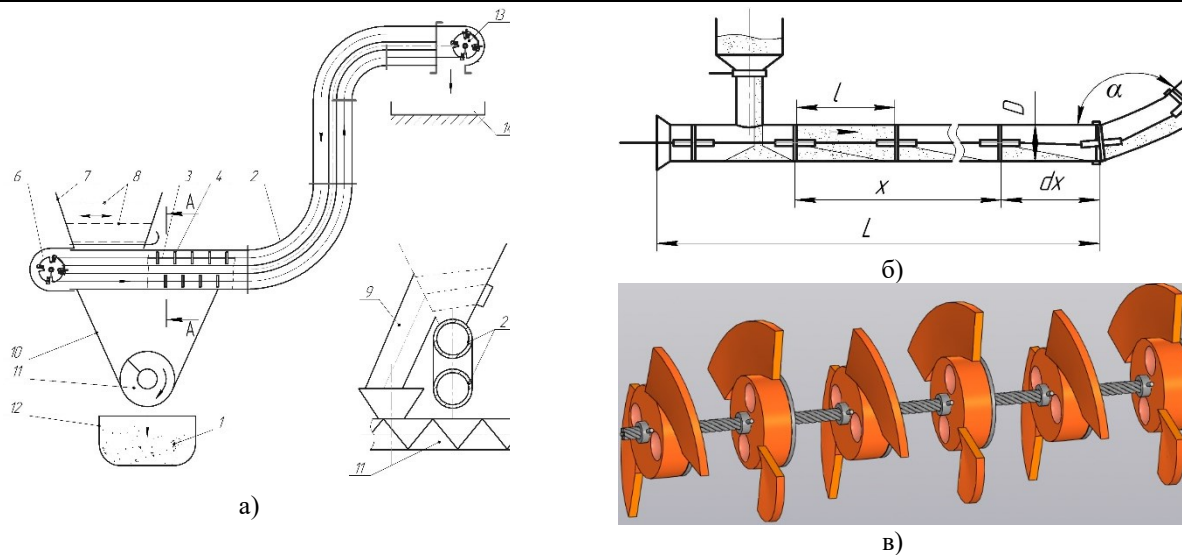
Схема трубчастого канатного скребкового конвеєра а) розрахункова схема горизонтальної гілки конвеєра б) модельований робочий орган; 1 - сипучий матеріал; 2 - S-подібні труби; 3 - робочий орган (ланцюг); 4 напрямні скребки; 5 - бочкоподібні скребки; 6, 13 - спеціальна приводна зірочка; 7 - завантажувальний бункер; 8 - робочий орган бункера; 9 - вихідна труба; 10 - бункер; 11 - шнековий робочий орган; 12, 14 - смість; 15 - з'єднувальна пружина скребків
